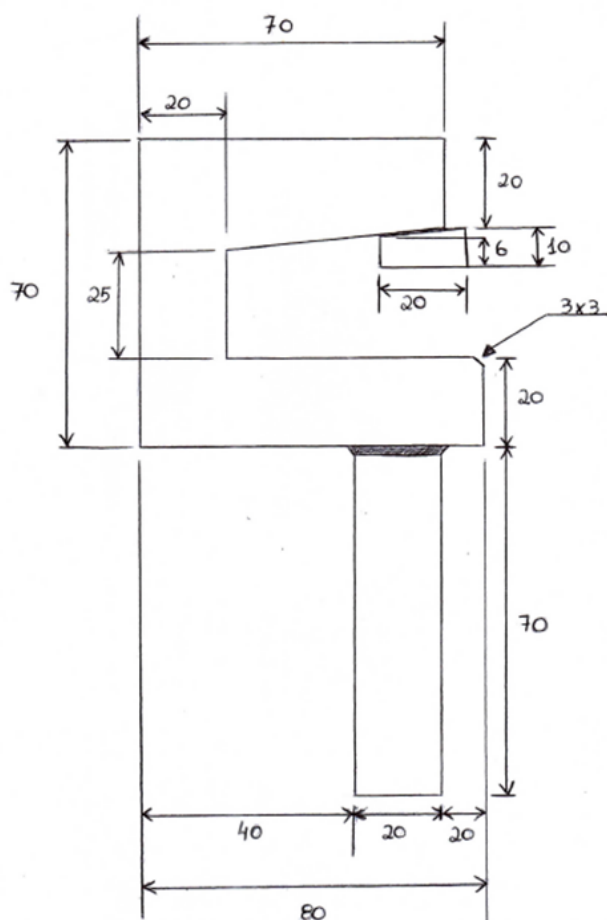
Projeto de detalhamento para fabricação da garra inferior.
